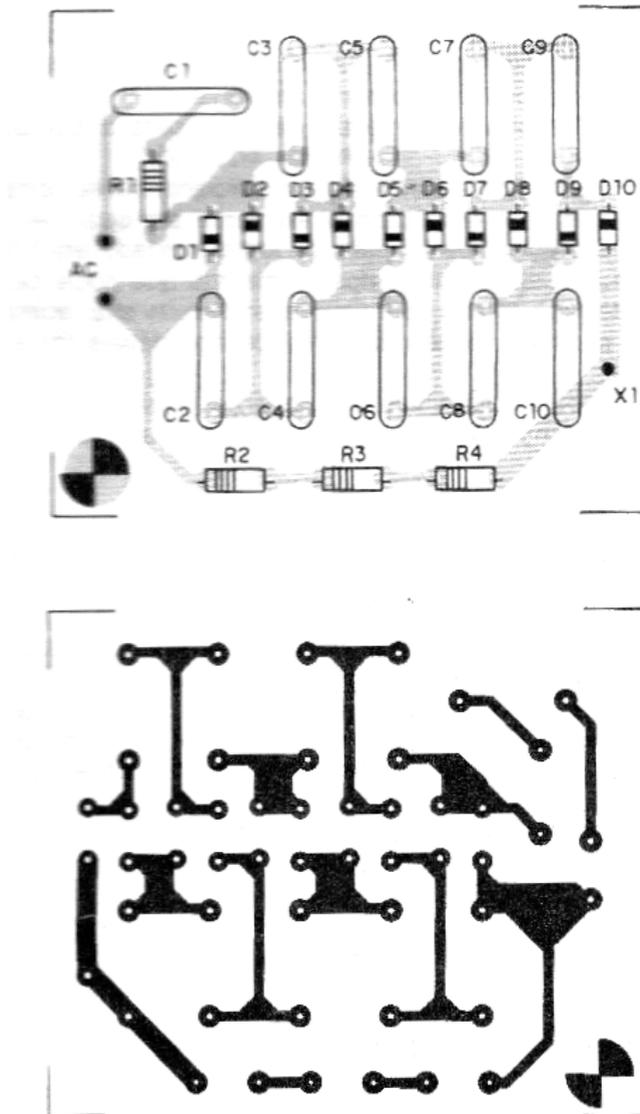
Montagem dos componentes numa placa de circuito impresso.
